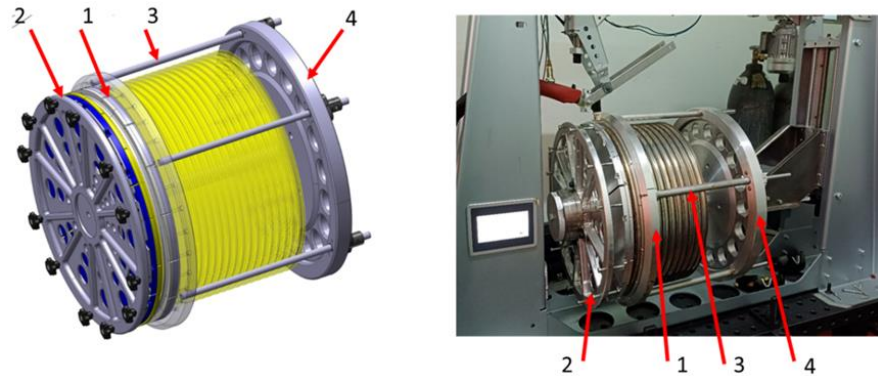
Пристрій для збирання та зварювання зовнішніх кільцевих швів.
